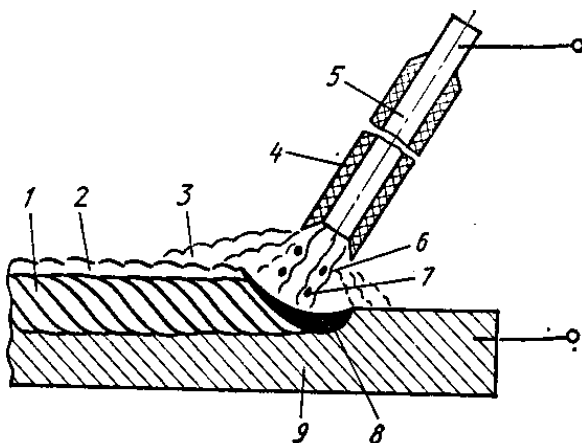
Схема ручного дугового зварювання металевим покритим електродом: 1 – шов; 2 – шлак; 3 – захисна газова атмосфера; 4 – електродне покриття; 5 – електрод; 6 – електрична дуга; 7 – краплі електродного металу; 8 – зварювальна ванна; 9 – заготовка
